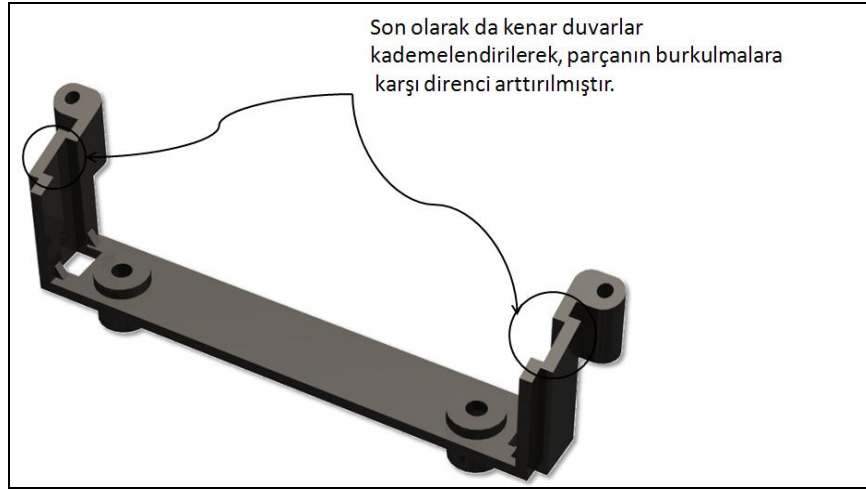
52 Side AV PCB tutucu bossları tasarımı
